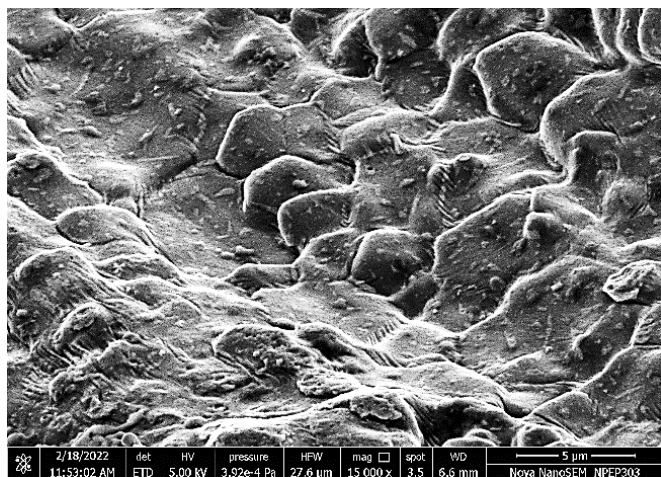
РЭМ-изображения поверхности излома UVaFSWed-соединений AA7075, подвергнутых дробеструйной обработке
